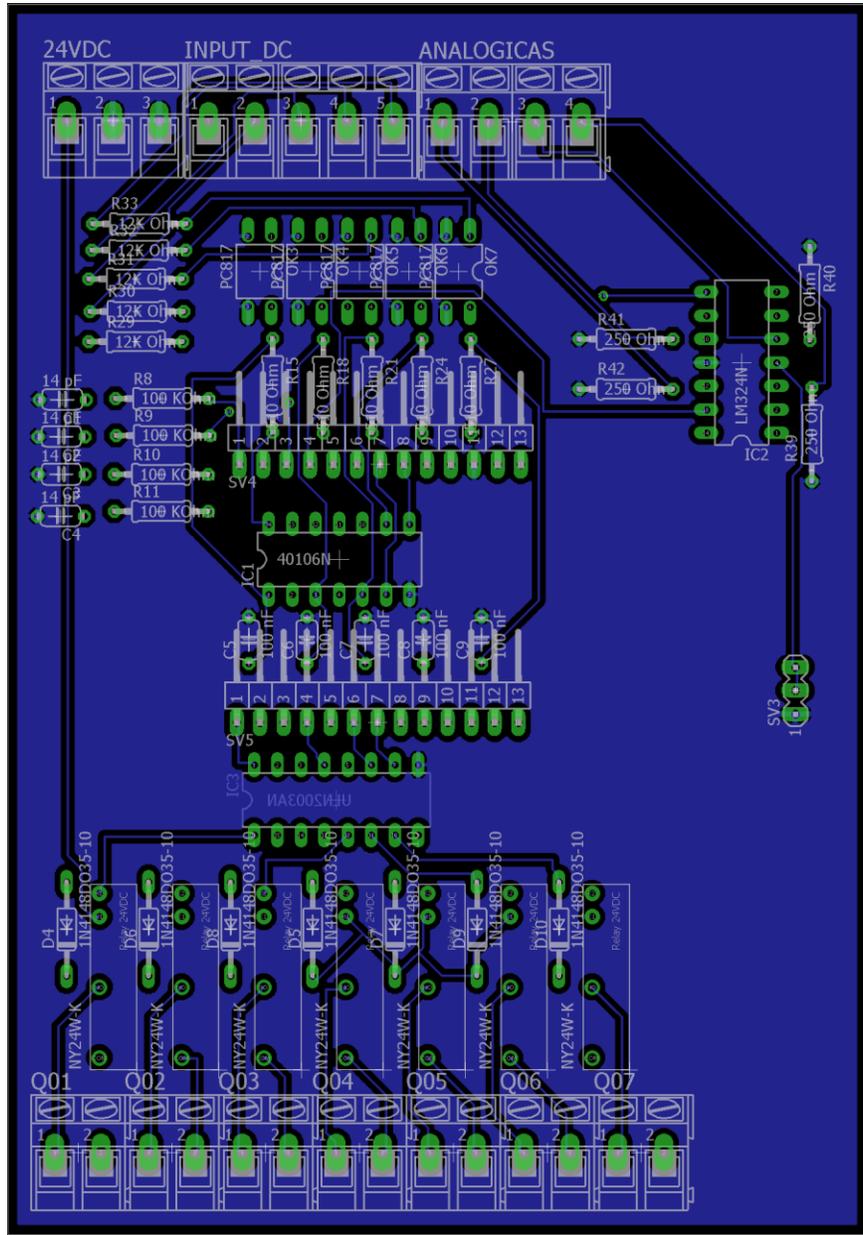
PCB CIRCUITO INTERFAZ IN/OUT - BOTTOM
